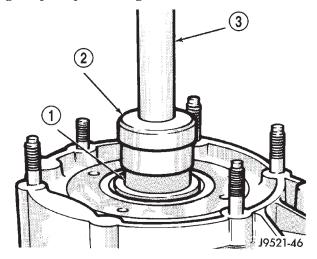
Desmontaje del conjunto del engranaje impulsor y de escala de baja
